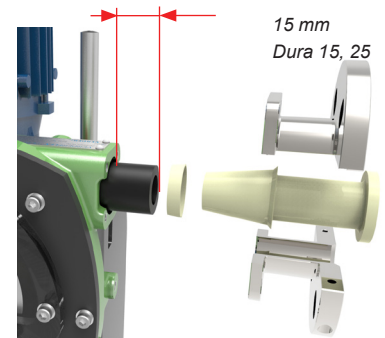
15mm Überstand (geteilter Flansch)
